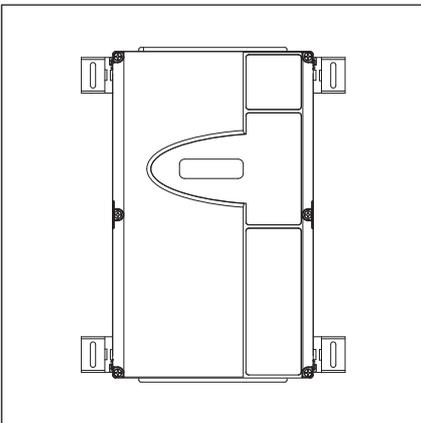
Steuerungsgehäuse mit horizontal befestigten Montagefüßen
